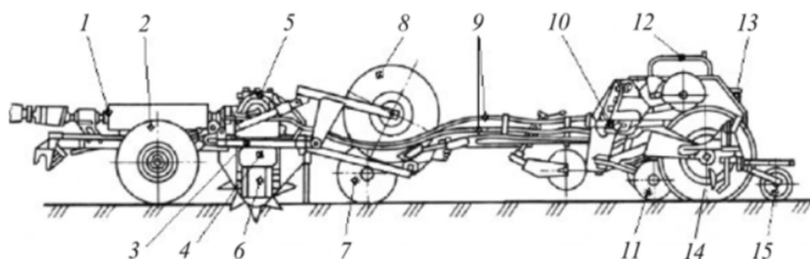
Агрегат для ускоренного залужения АЗ-2,4: 1 – промежуточный вал; 2 – опорное колесо; 3 – сварная рама; 4, 5 – редуктор; 6 – фрезерный барабан; 7 – каток; 8, 14 – транспортное колесо; 9 – гидросистема; 10 – рама сеялки; 11 – двухдисковый сошник; 12 – зерновой ящик; 13 – травяной ящик; 15 – прикатывающее колесо.
